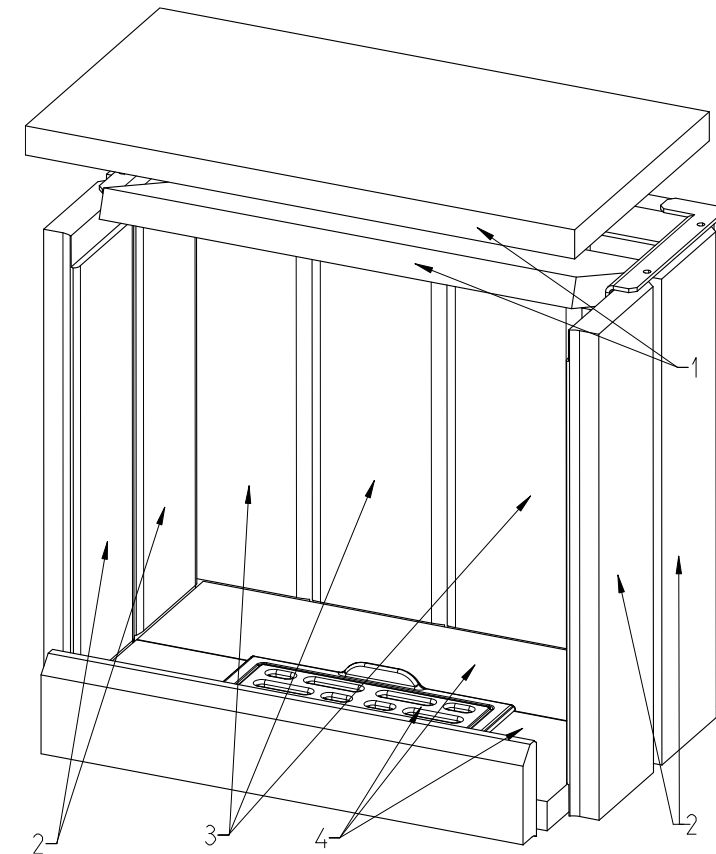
D, Zeichnung 3D, Croquis 3D, Ingombro 3D
